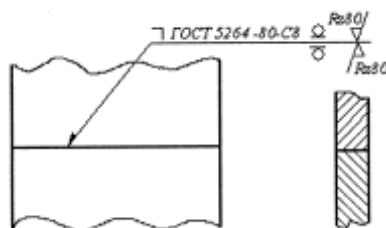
Шов выполнен при монтаже (∇) ручной дуговой сваркой по ГОСТ 5264-80, тип шва)С9),
